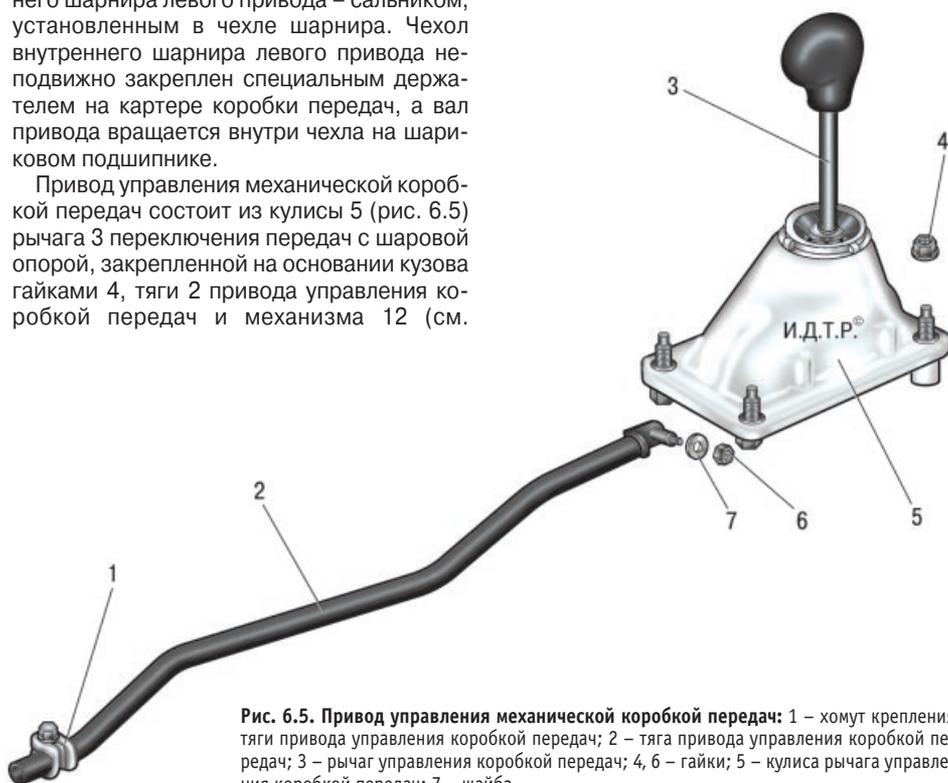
Привод управления механической коробкой передач: 1 – хомут крепления тяги привода управления коробкой передач; 2 – тяга привода управления коробкой передач; 3 – рычаг управления коробкой передач; 4, 6 – гайки; 5 – кулиса рычага управления коробкой передач; 7 – шайба
